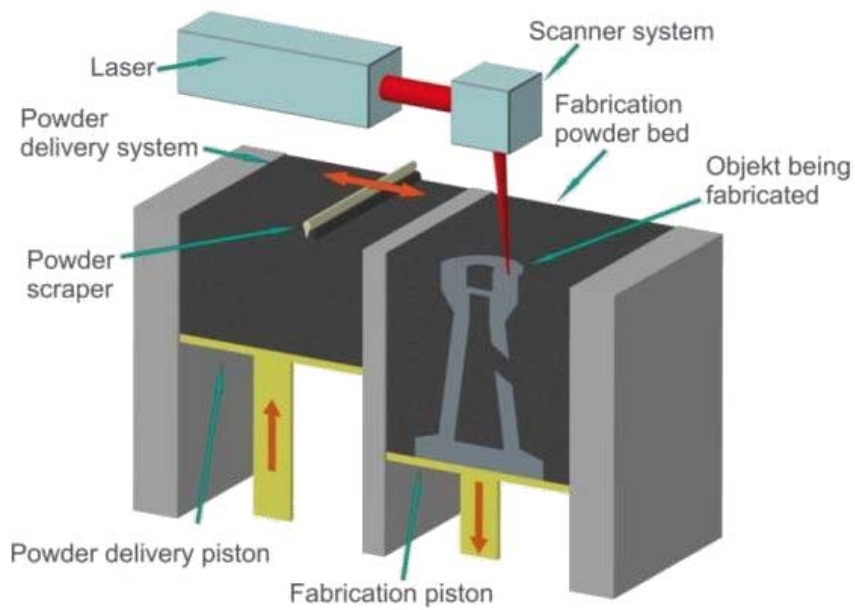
Prinzip einer Laser Pulverbett-Anlage
